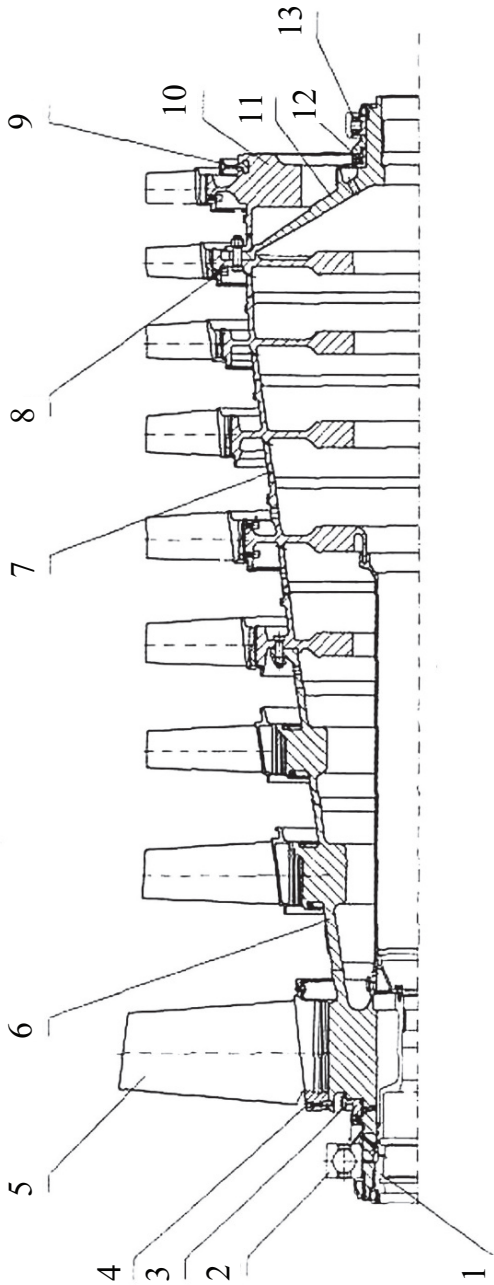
Ротор компрессора низкого давления ГТД ДН80:
